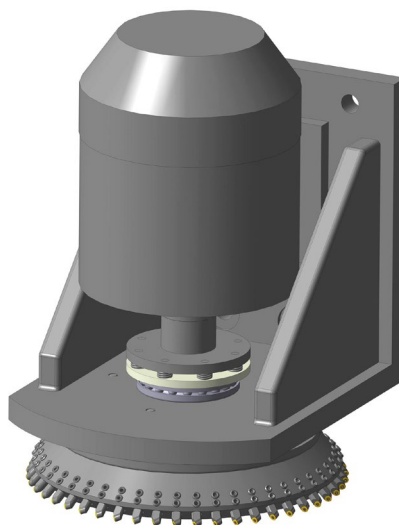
Агрегатна фрезерна головка, що містить торцеву фрезу з циліндричними різальними вставками та кріпильними гвинтами з конічними ділянками
